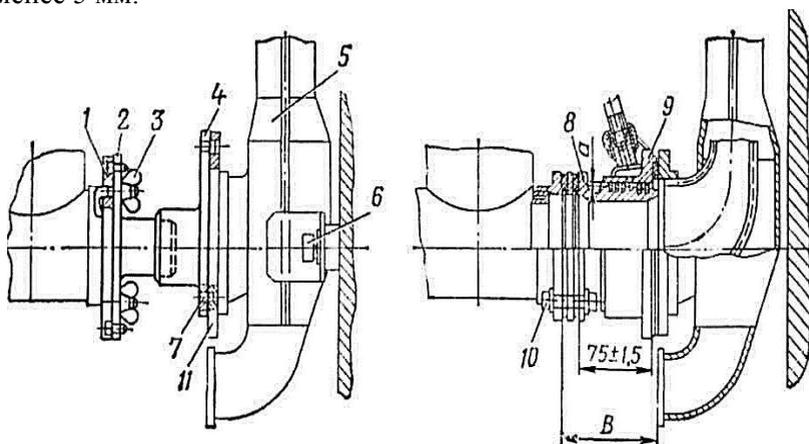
Установка приспособления 175.95.007С6 для центровки выпускных труб с выпускными коллекторами танка Т-72:
